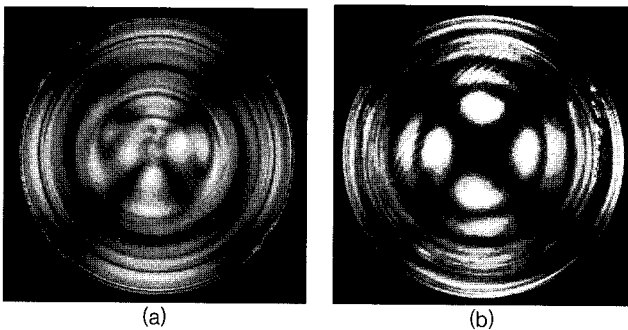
Comparison of the birefringence pattern of injection molded and compression molded preforms: (a) injection molded preform; (b) compression molded preform.
